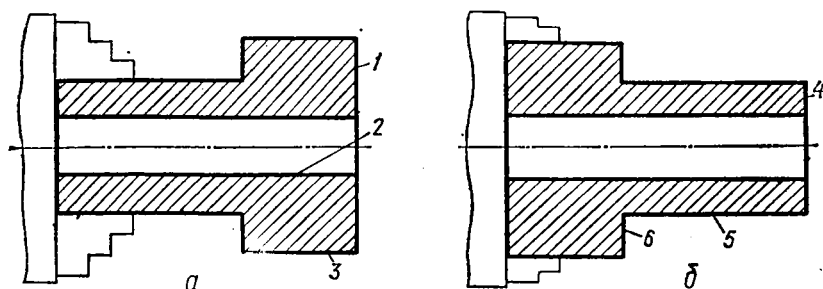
Схема установки втулки для обработки в патроне токарного станка
